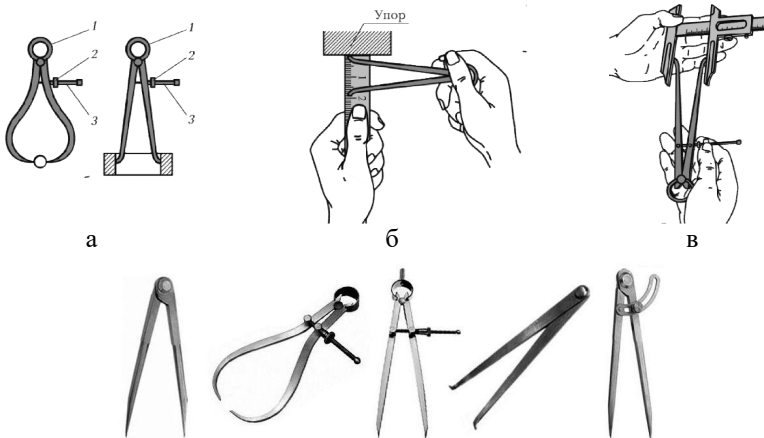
Кронциркулі: а – пружинний для зовнішніх та внутрішніх вимірів: 1 – пружина; 2 – гайка; 3 – гвинт; б, в – вимірювання розміру по кронциркулю з використанням вимірювальної лінійки та штангенциркуля
